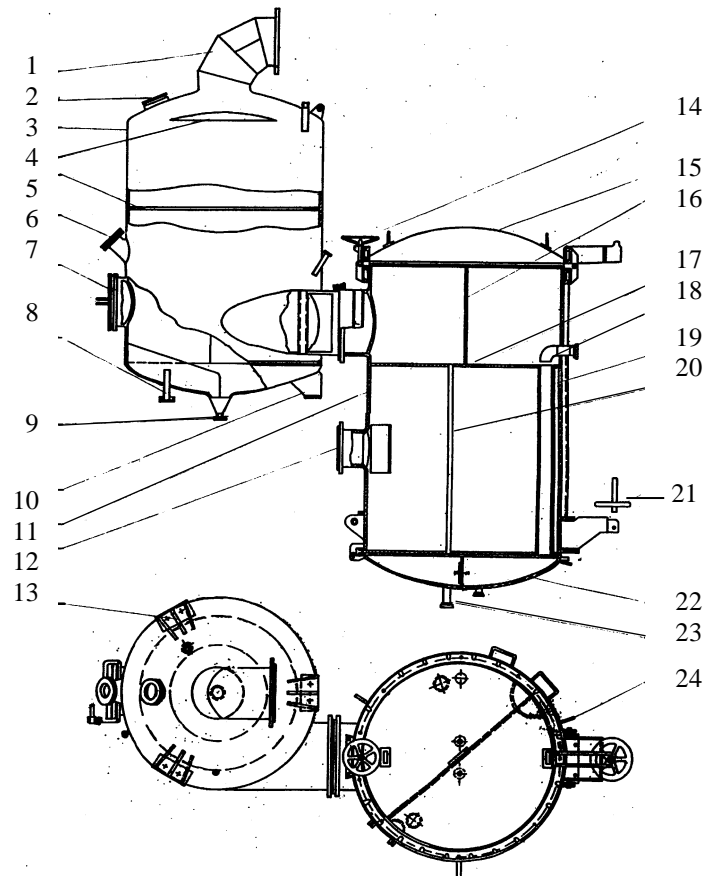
Загальний вид корпусу вакуум-апарата
